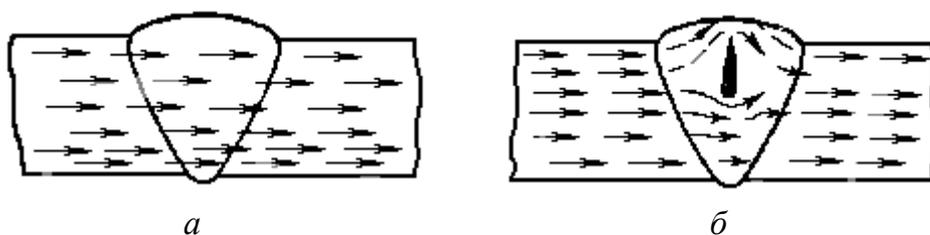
Путь линий магнитного потока при прохождении через сварной шов:
